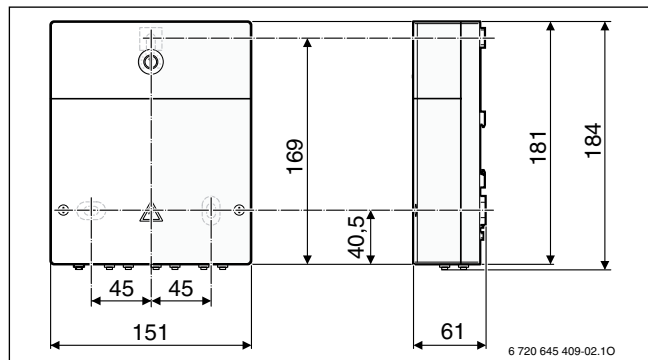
Размеры модуля контура отопления или ГВС MM100 (размеры в мм)
